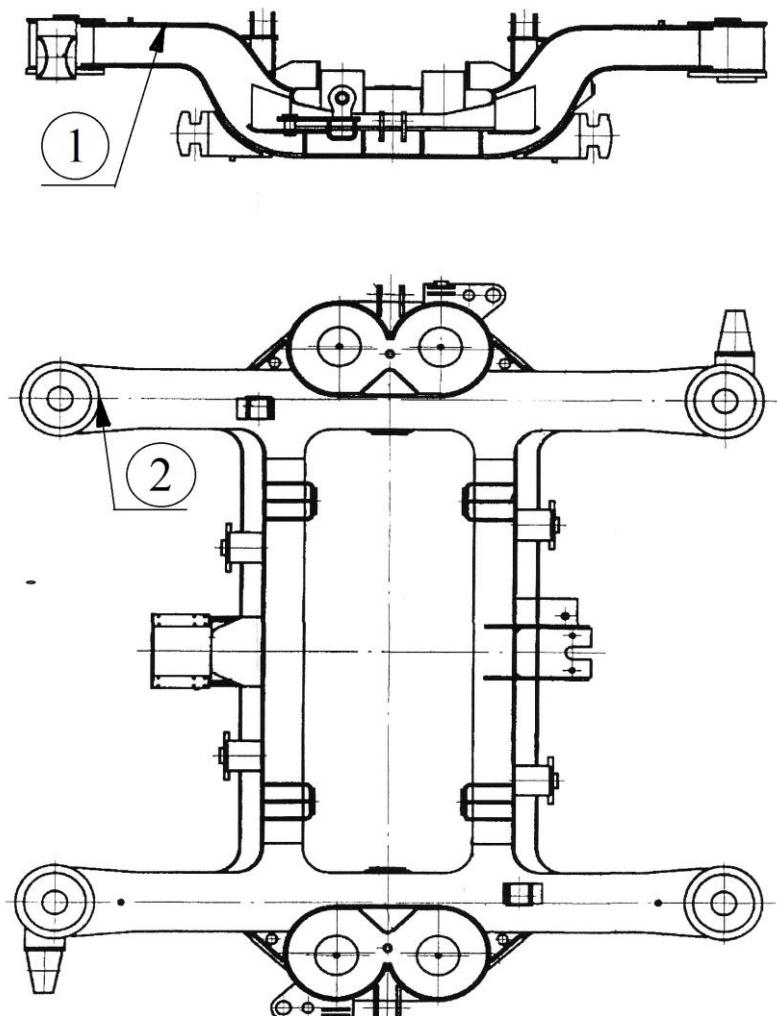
Основные дефекты рамы тележки пассажирского вагона 68-4096, ремонтируемые сваркой или наплавкой
